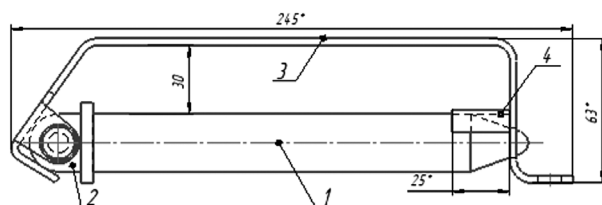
Общий вид доработанного быстроразъемного шарнира: 1 — ось; 2 — рым пальца; 3 — стопорная ручка; 4 — ограничитель
